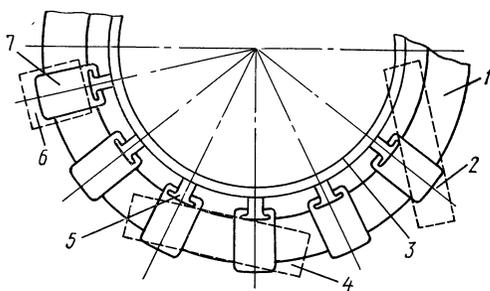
Подготовка к стяжке и прессовке обмоток:
